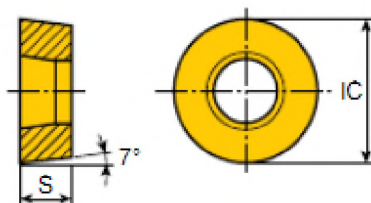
Пластина RCMX 160600 CVD покриття : TT8125B
